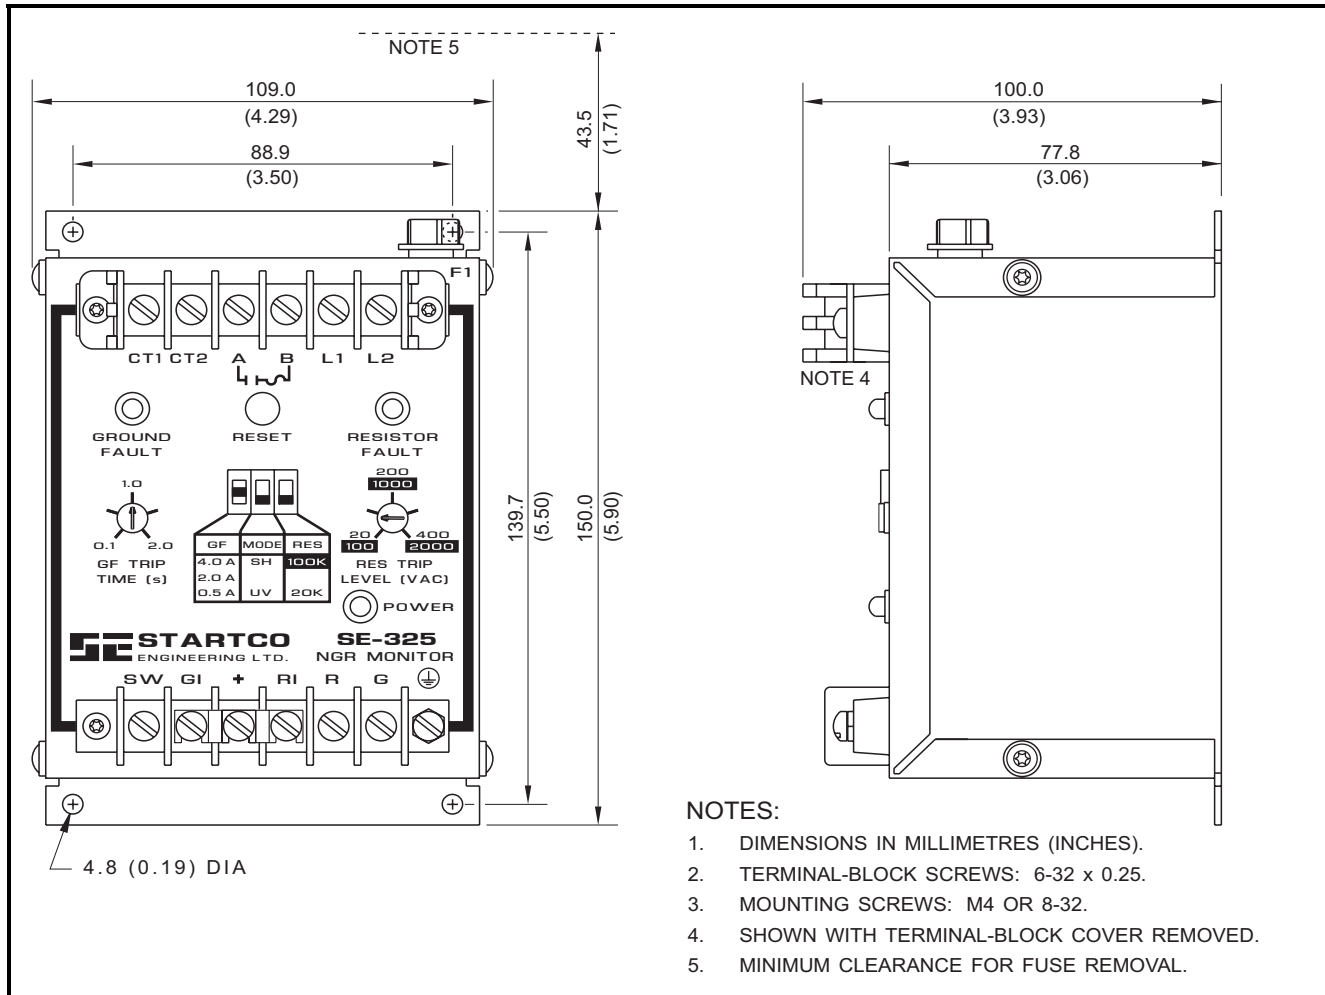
Габаритные размеры SE-325 и информация об установке.
